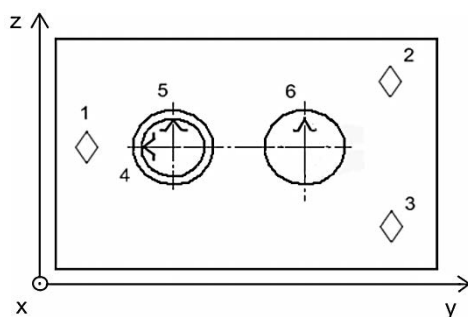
Елементи базування деталі типу «Корпус» (виділені зеленим кольором).
